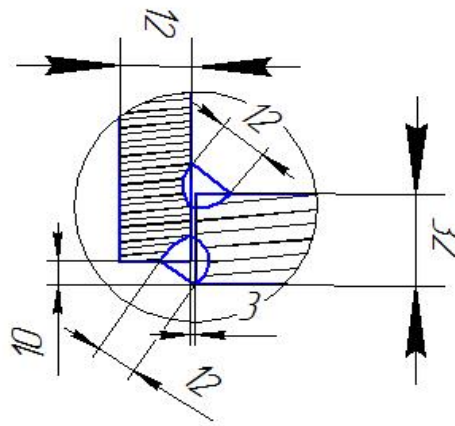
Параметры сварных швов соединения У5
